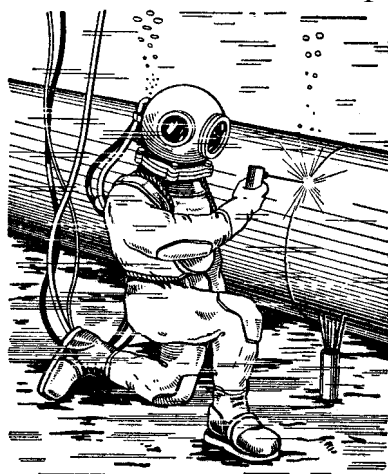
Сварка стыка трубопровода под водой.
